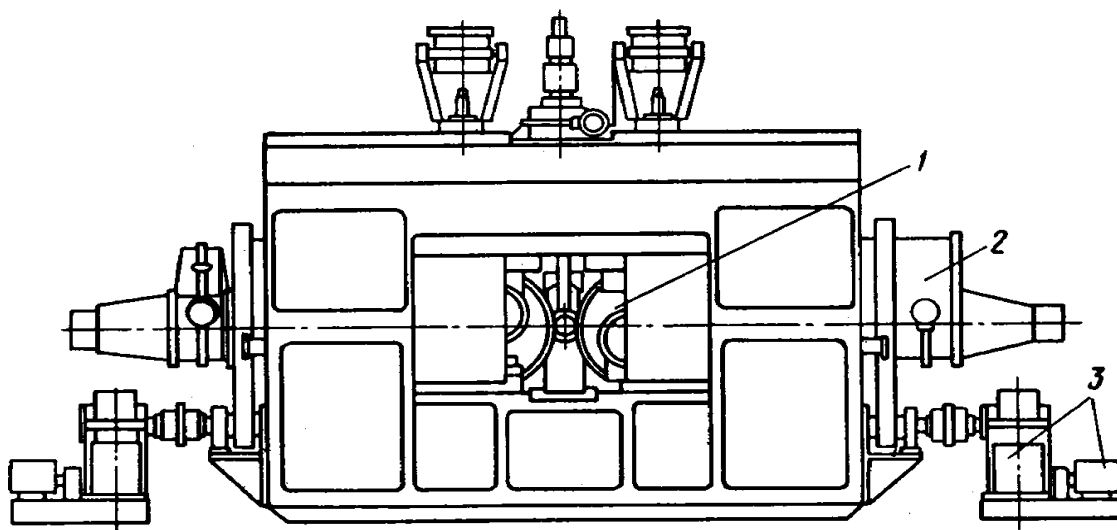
Рабочая клетка прошивного стана с бочковидными валками
